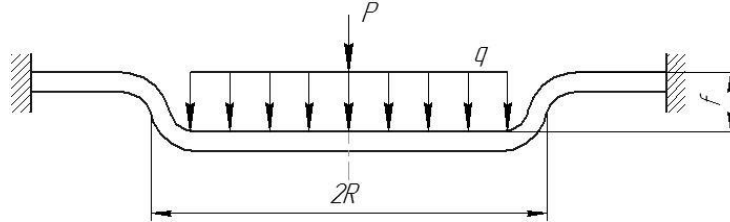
Схема деформування листової заготовки циліндричним пуансоном
